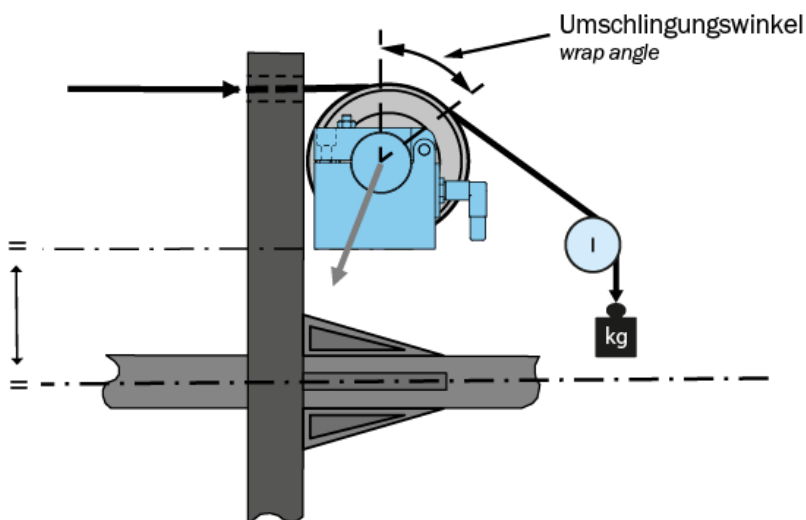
Beaufschlagen des Kraftaufnehmer mit einer definierten Gewichtskraft
